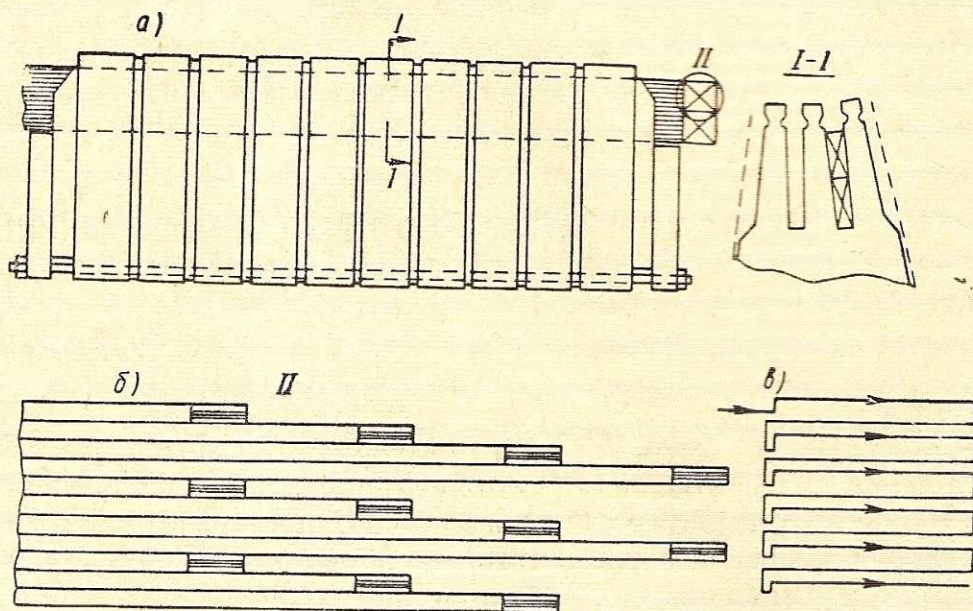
Эскиз установки стержней в пазу пакета стали статора: а — пакет стали с пазами; б — лобовая часть стержня; в — схема соединения элементарных проводников.
